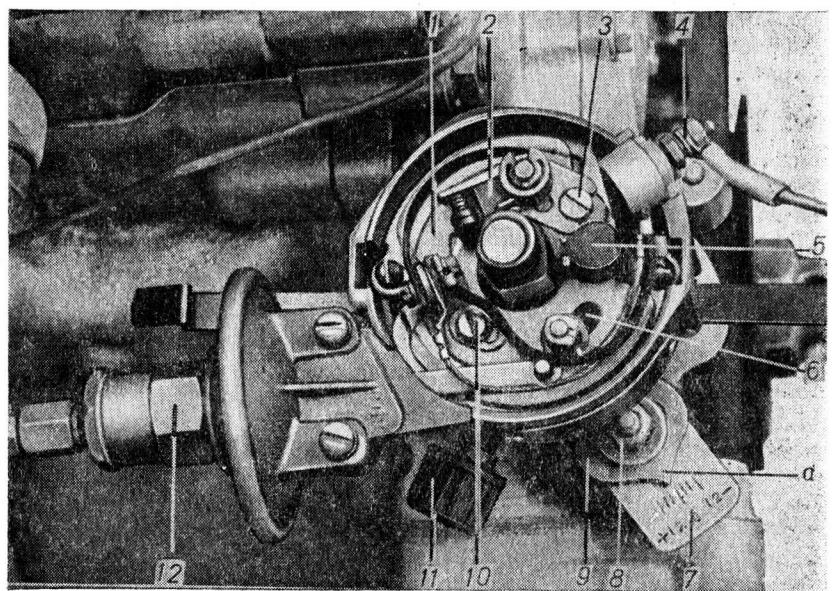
Распределитель зажигания типа Р118 со снятыми крышкой и ротором:
